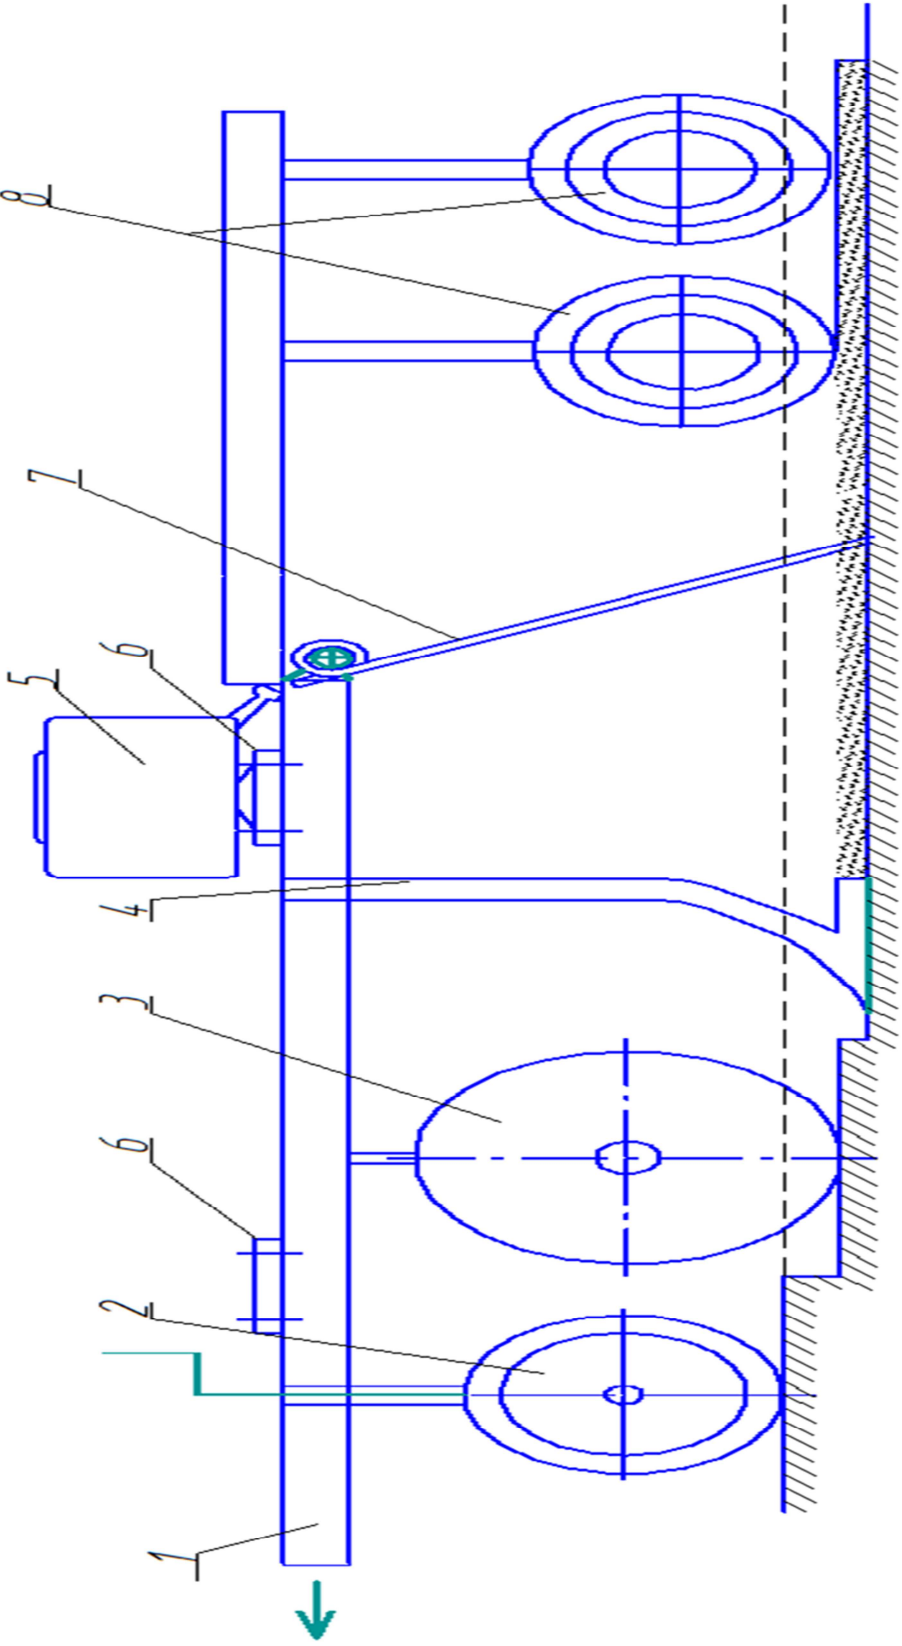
Многоцелевой комбинированный почвообрабатывающий агрегат
